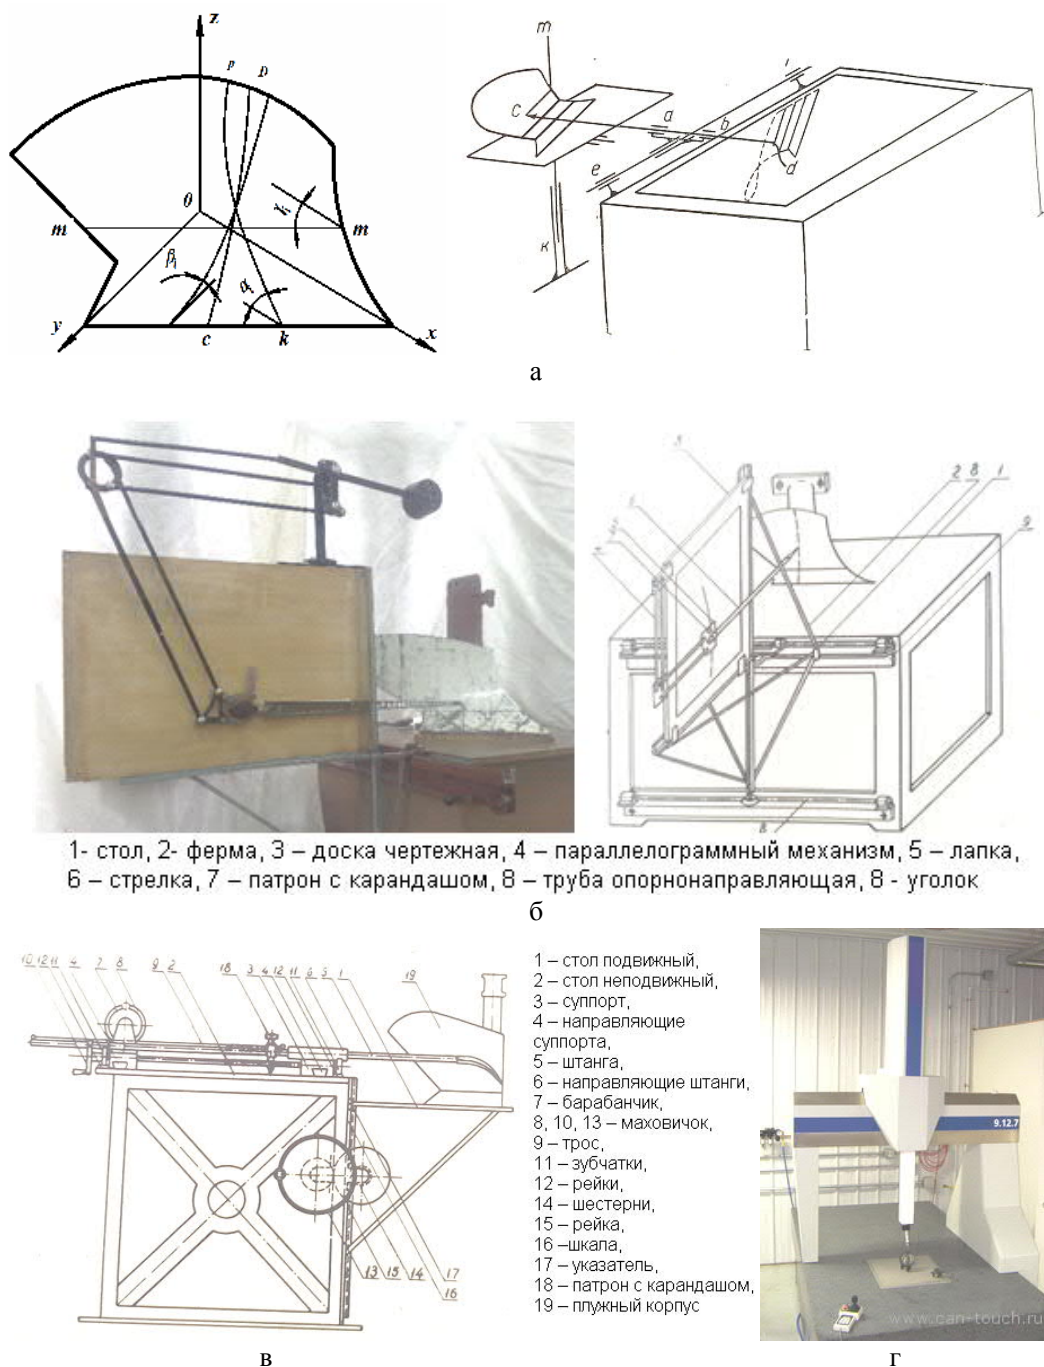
Схемы и общий вид профилографов, координатно-измерительных столов и машин различной конструкции для реверс-инжиниринга рабочих органов совершенствуемых почвообрабатывающих машин с криволинейной поверхностью: а – В.П. Горячкина; б - М.Х. Пигулевского; в - Е.В. Козловского; г – цифрового типа с автоматизированным устройством.
